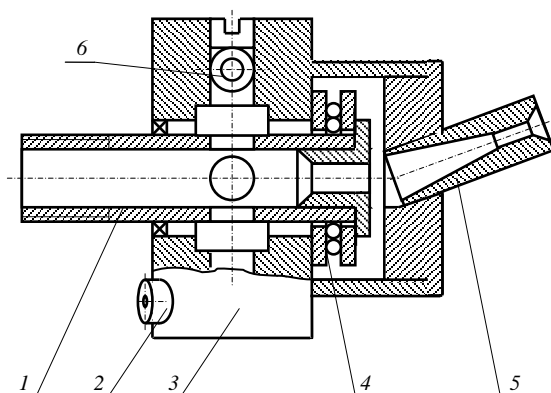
Головка с вращающимся корпусом: 1 – штуцер; 2 – заднее сопло; 3 – корпус; 4 – подшипниковый узел; 5 – переднее сопло; 6 – тангенциальное сопло
